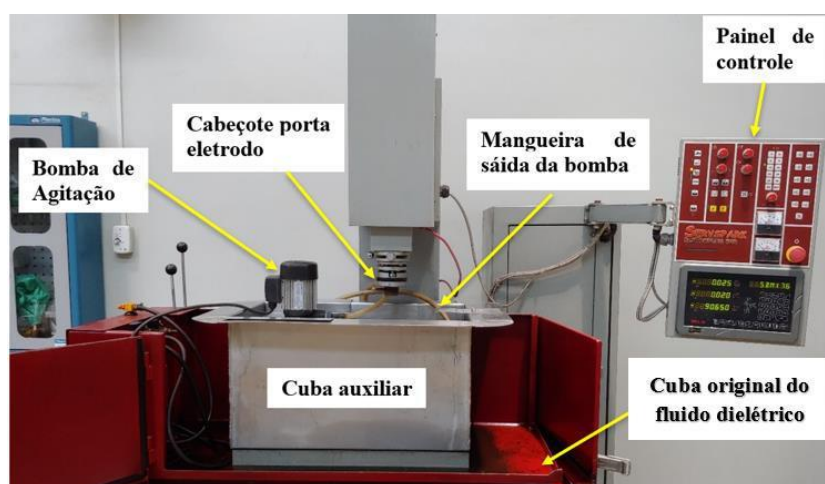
Máquina de EDM adaptada que foi utilizada nos testes.
